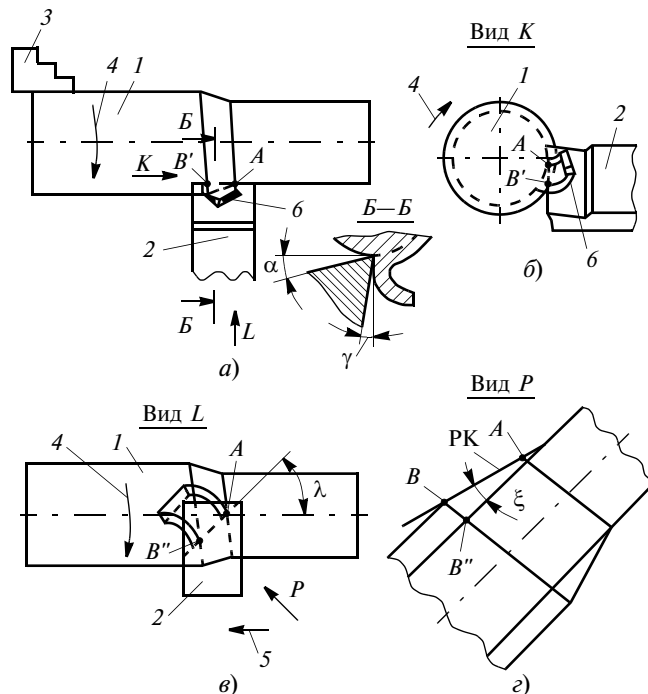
Схема обработки деталей БПТР (а) и взаимные положения БПТР и заготовки: вид К (б), вид L (д), вид Р (е)
